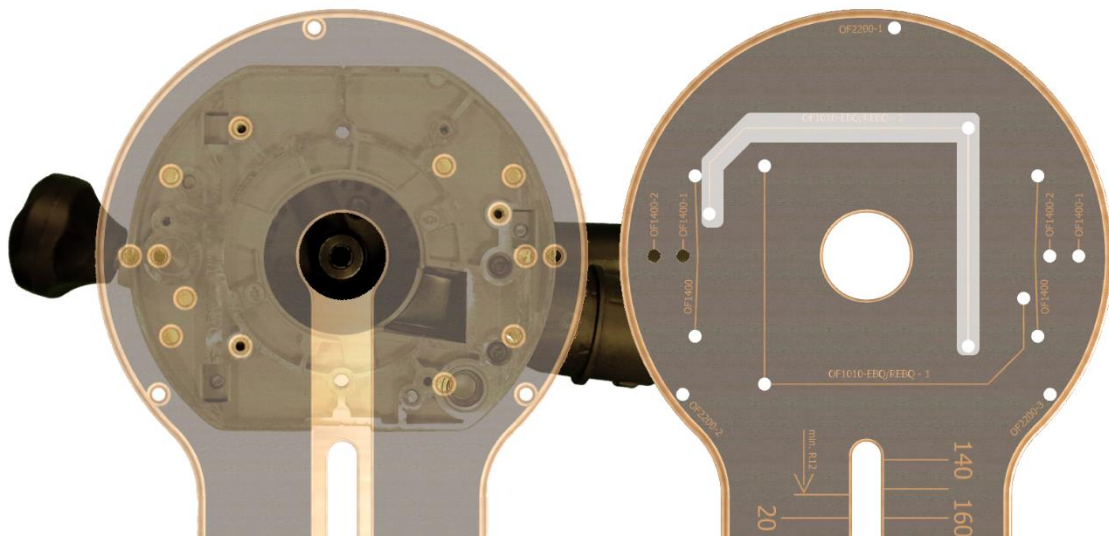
Fori di montaggio 2 adatti al Festool OF1010-REBQ
